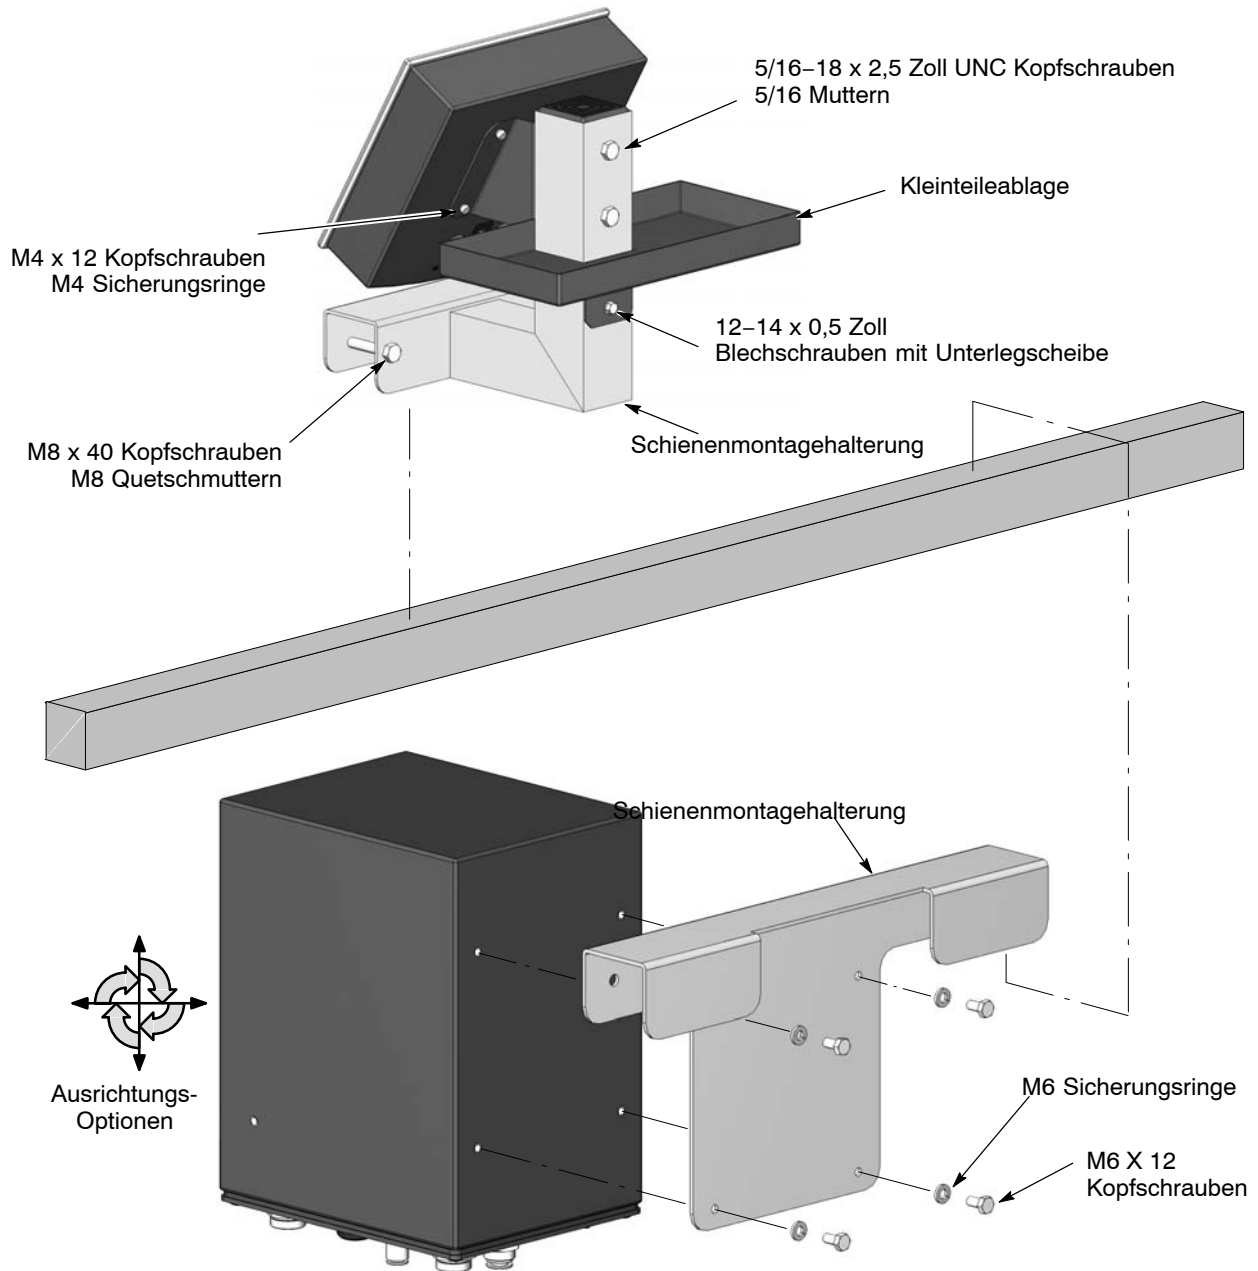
Schienenmontagehalterungen für Steuerung
